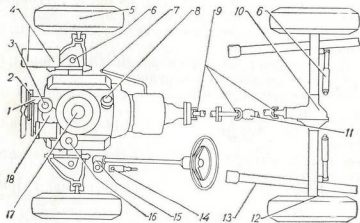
Точки смазки шасси и двигателя автомобиля.
